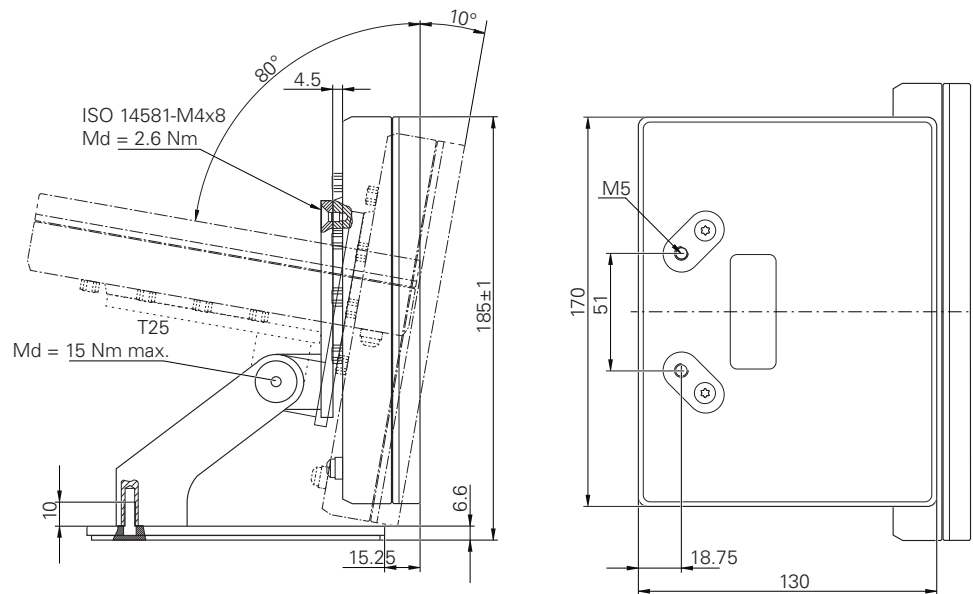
Dimensiones del aparato con pie de soporte Multi-Pos
